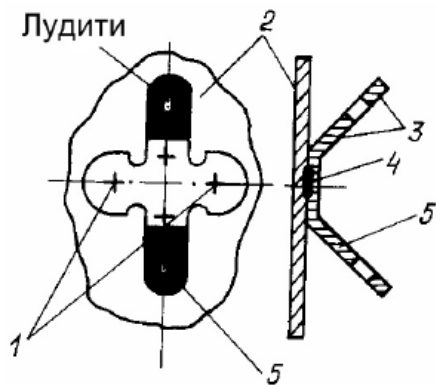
Контакт пелюсток з плакованого алюмінію, що з'єднується з алюмінієвим корпусом точковим контактним електрозварюванням: 1 – місце зварювання; 2 – корпус; 3 – лужена ділянка пелюстки; 4 – плакований шар міді; 5 – пелюстка
